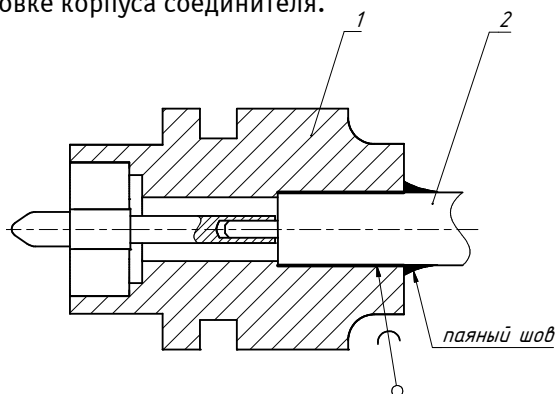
Монтаж кабеля к корпусу кабельного соединителя
